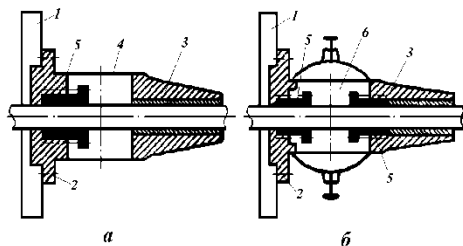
Схема конструкцій цапф з одинарним (а) і подвійним (б) ущільненнями: 1 – торцева стінка корпусу; 2 – фланець; 3 – опорна частина цапфи; 4 – вікно; 5 – сальникове ущільнення; 6 – сальникова коробка
